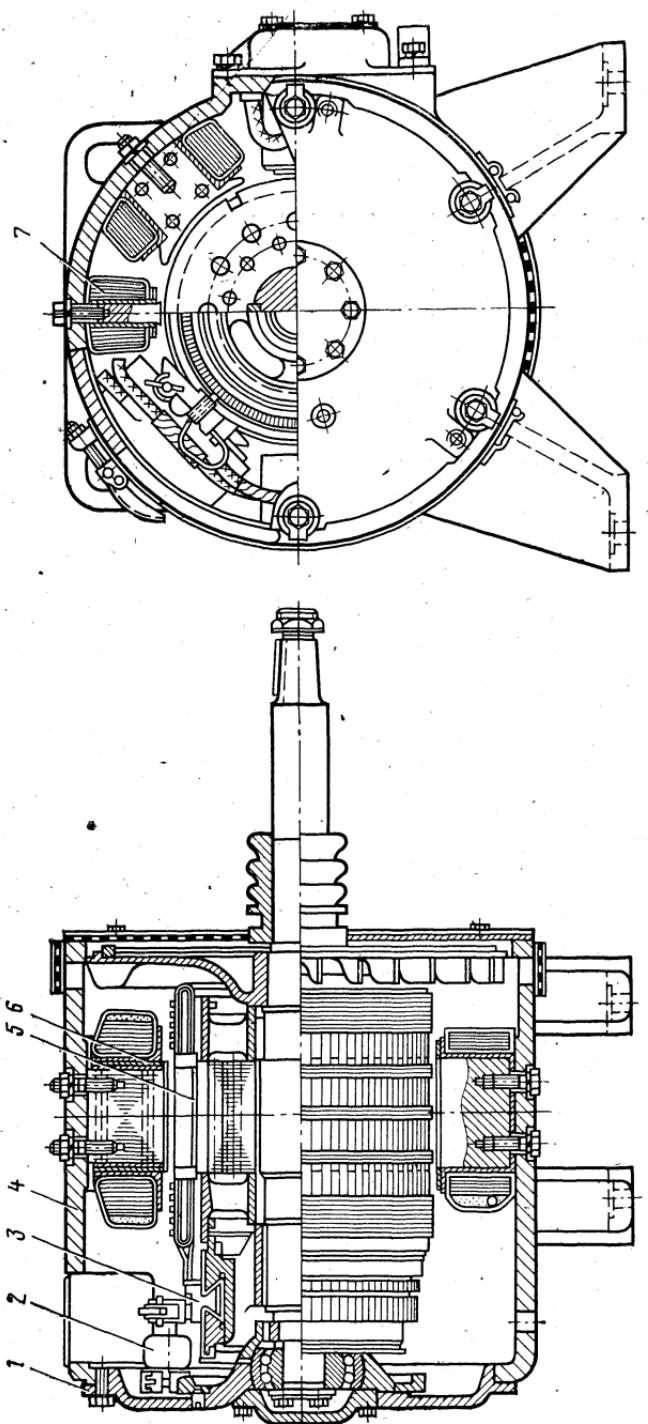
Продольный и поперечный разрезы электродвигателя НБ-404А
